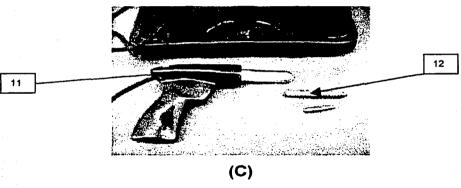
Descripción de las partes de una soldadora eléctrica
